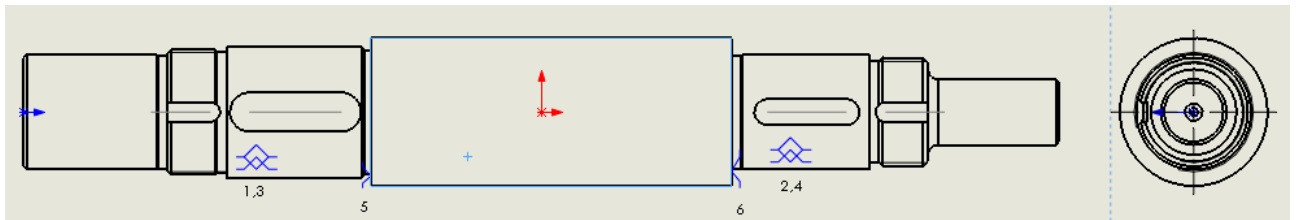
Теоретична схема базування для обробки поверхонь 16, 17,18,19.
